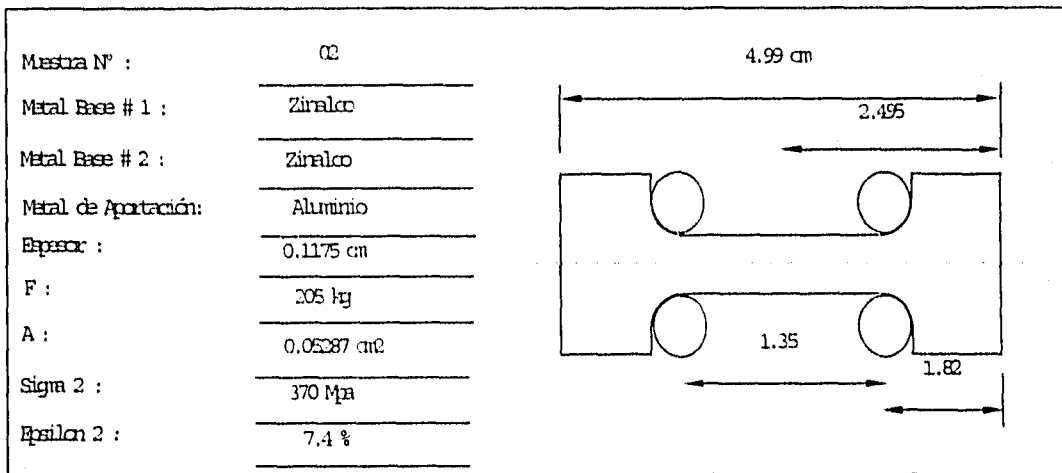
Probeta No.2, valores de prueba a la tensión para soldadura realizada entre Zinalco y Zinalco con material de Aporte Aluminio.
